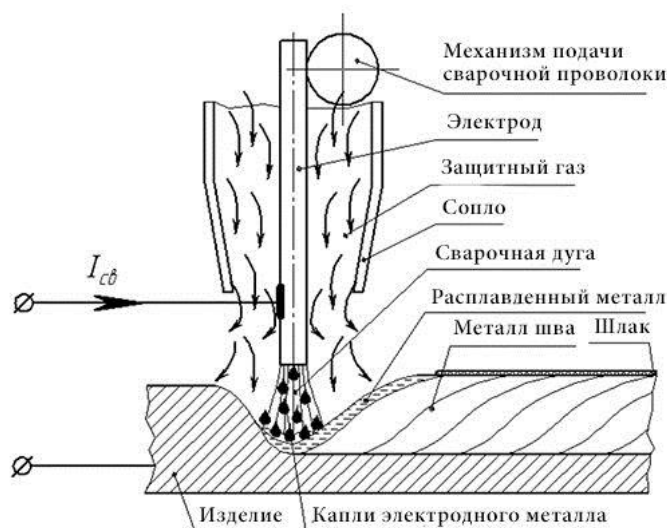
Схема осуществления механизированной сварки в среде защитного газа
